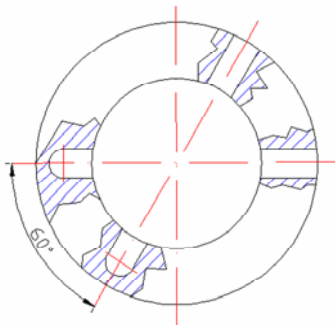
Takım tutucunun dış kısmının şematik görünüşü (The schematic illustration of outer side of tool holder)
